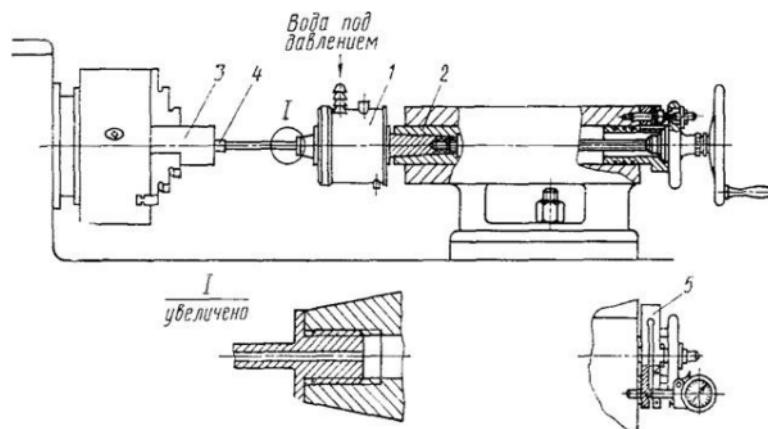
Схема экспериментальной установки: 1 – ультразвуковая головка; 2 – пиноль задней бабки; 3 – обрабатываемая заготовка; 4 – алмазное сверло; 5 – динамометрическая скоба
